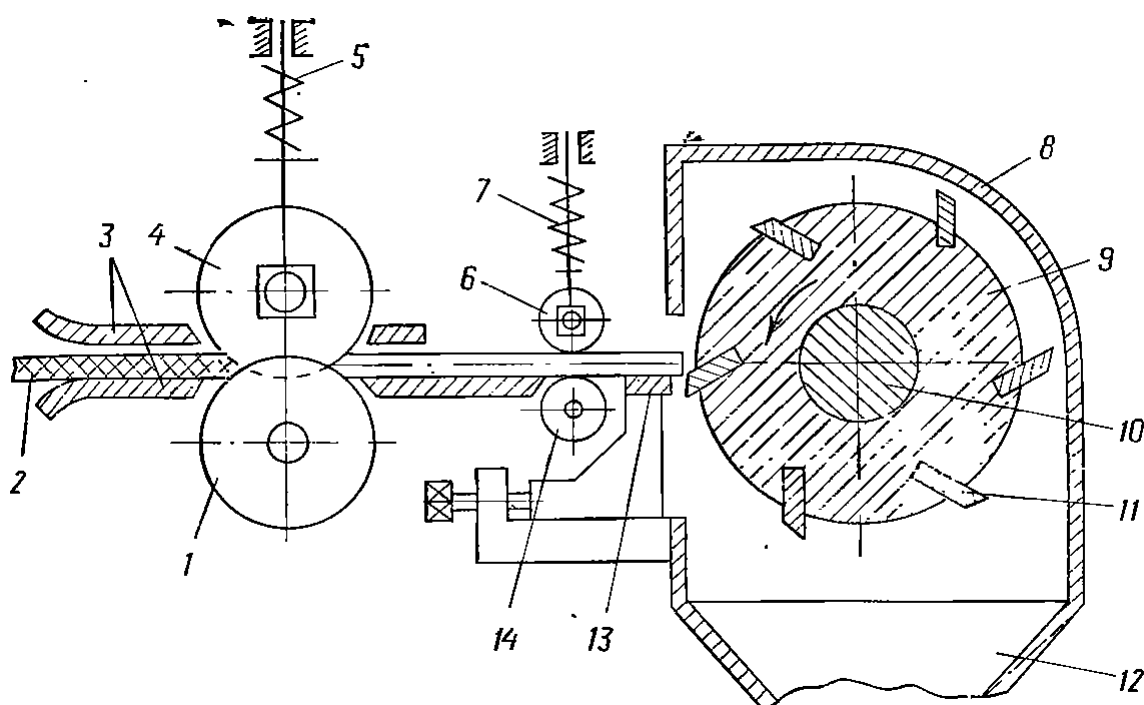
Дробилка с дисковыми ножами и режущим ротором («дайсер»):
